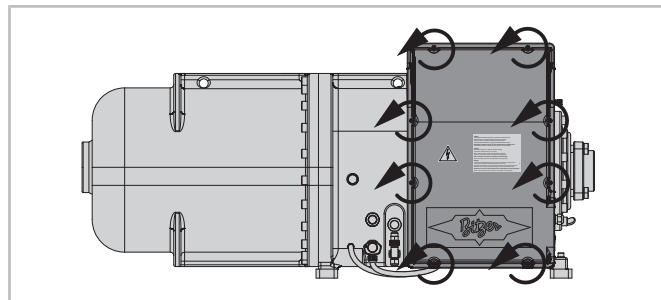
CSV.2: Снятие крышки корпуса FI.
